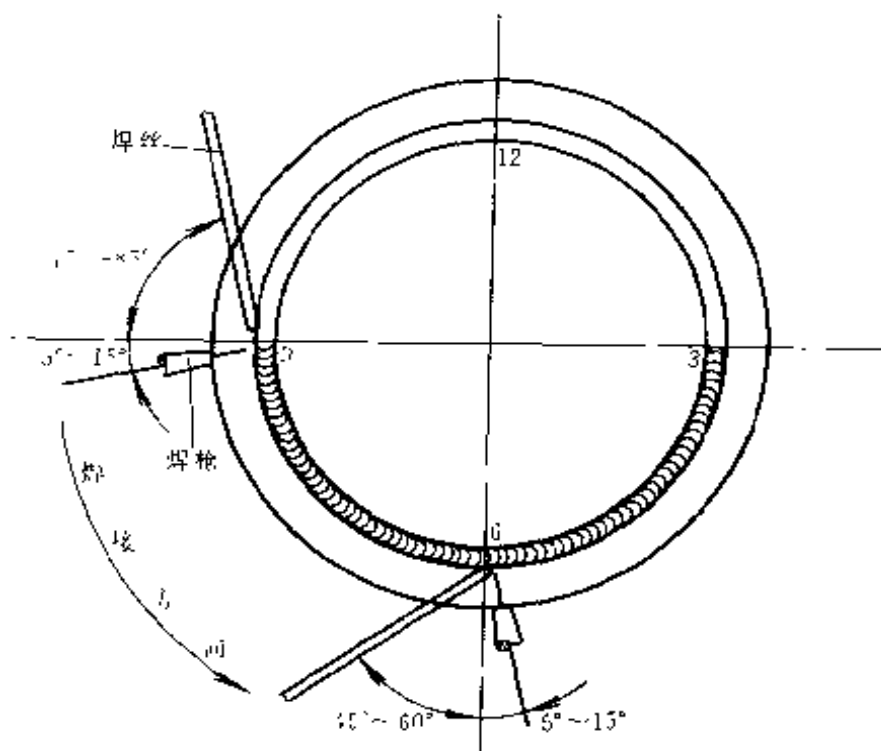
小管水平固定左半部立向下 9 点位置至 6 点位置外填丝 TIG 焊
